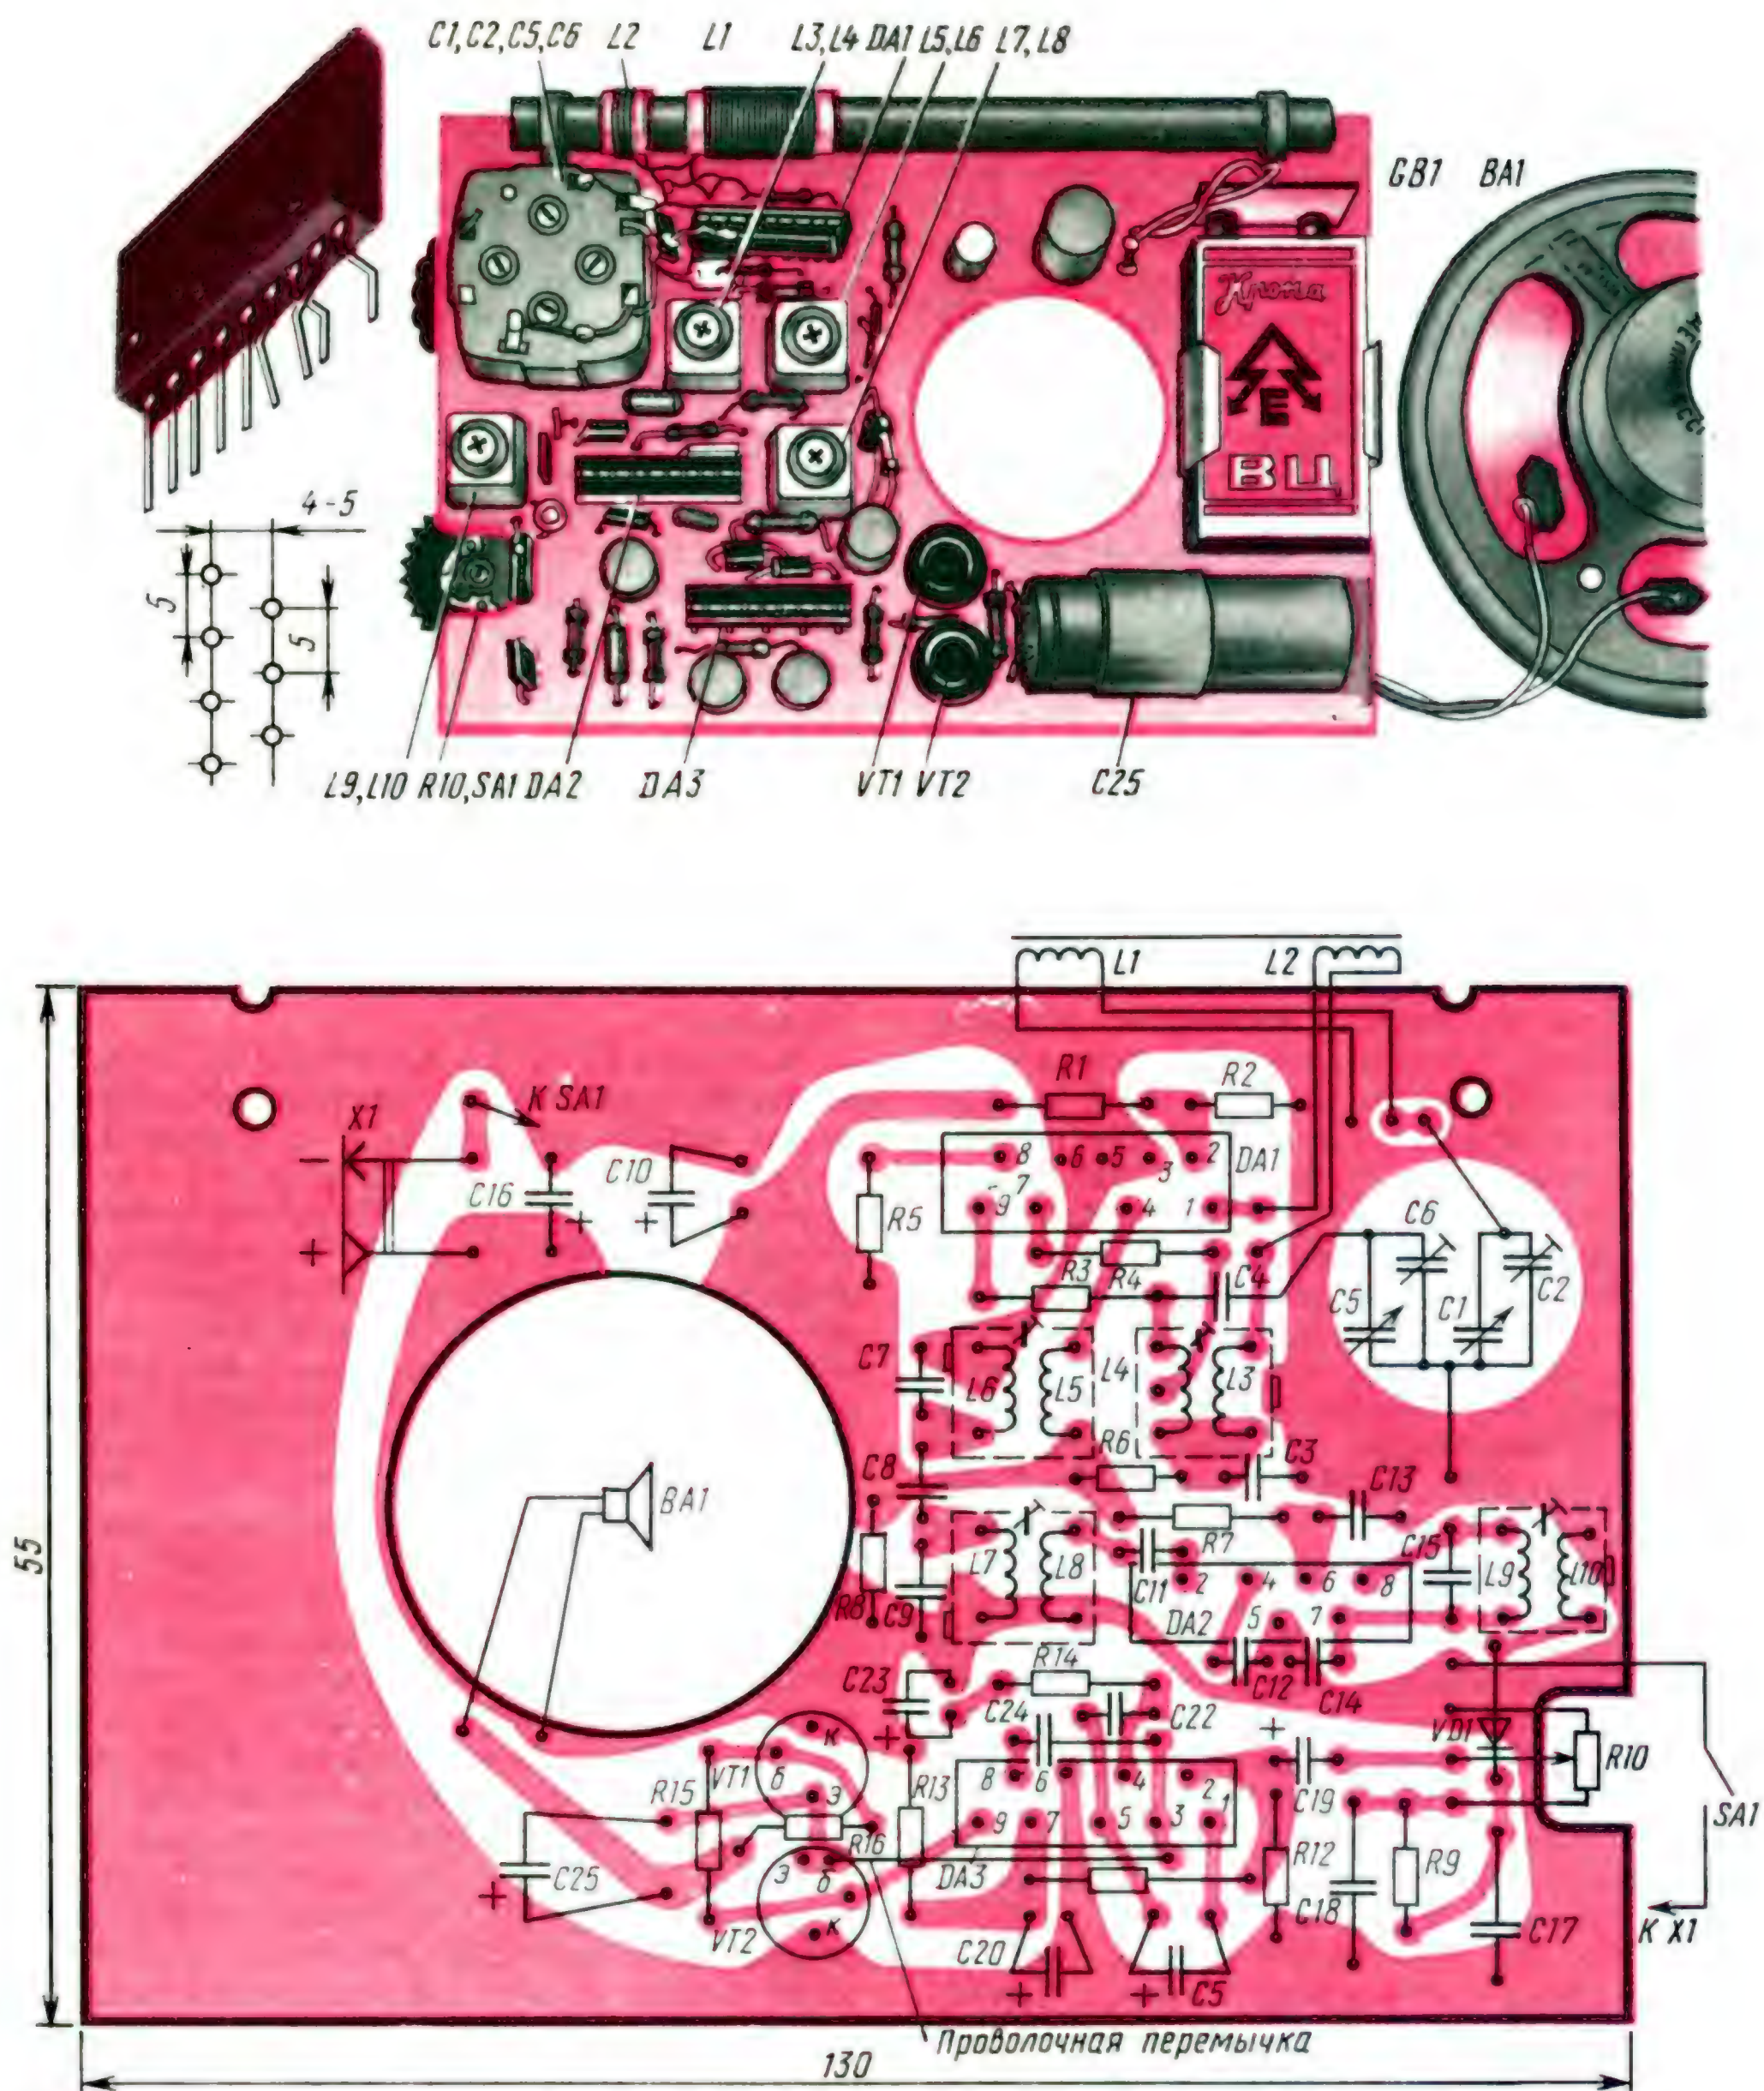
Монтаж деталей, разметка токонесущих проводников печатной платы и схема соединений на ней
